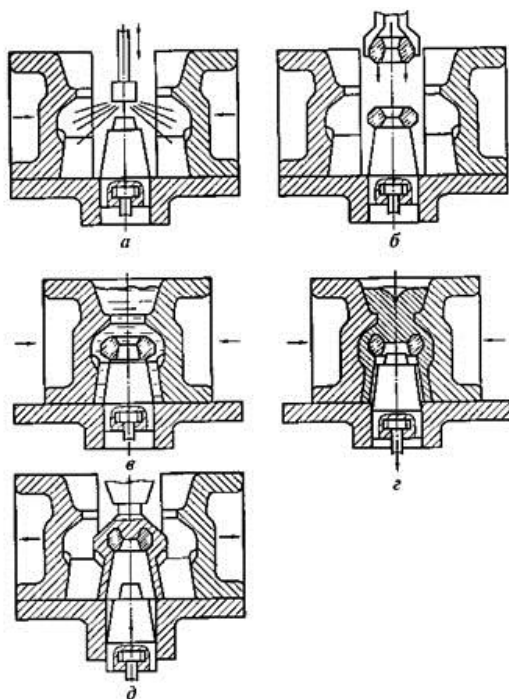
Основные операции и процессы изготовления отливки в кокиле: а – очистка полуформ; б – установка стержней; в – заливка расплава; г – частичное удаление металлического стержня; д – извлечение отливки; стрелки – направление движения деталей кокиля
